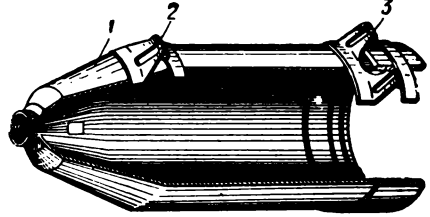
Корпус двигателя с узлами крепления, установленными на цилиндрической части ракетной камеры:
